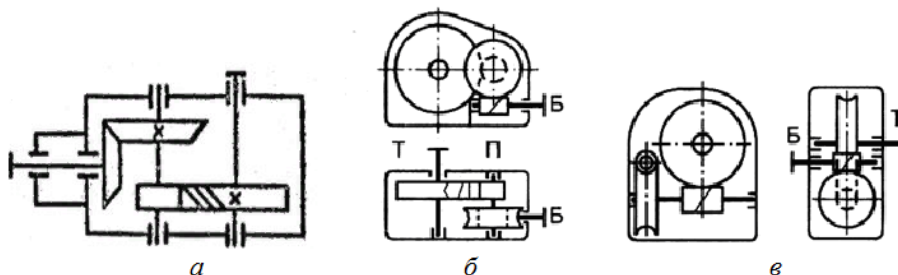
Схемы двухступенчатых редукторов: *а* – коническо-цилиндрический; *б* – червячно-цилиндрический; *в* – червячно-червячный
